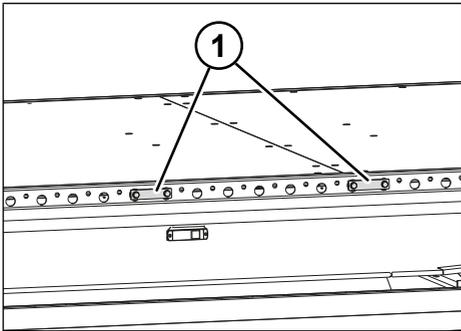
Butée fixe Multi Belt sur cadre extérieur Multi Lock
